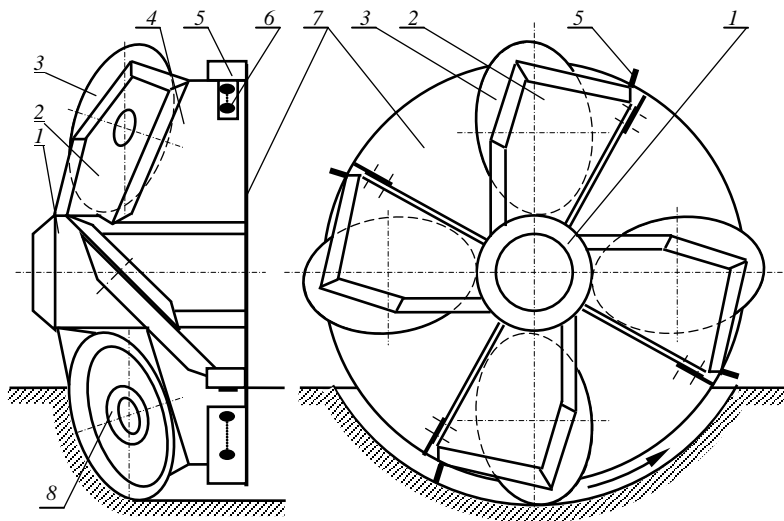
Схема фрезерного рабочего органа с дисковыми ножами: 1 – ступица; 2 – кронштейны; 3 – ножи; 4 – лопатки; 5 – плоские ножи; 6 – болты; 7 – диск фрезы; 8 – центральные болты
